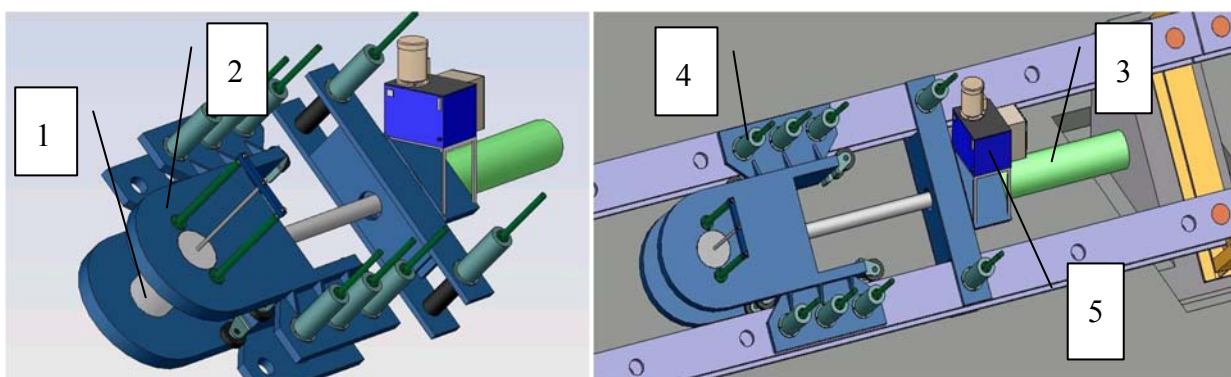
Primeiro esboço do sistema automático de pré-tensionamento
